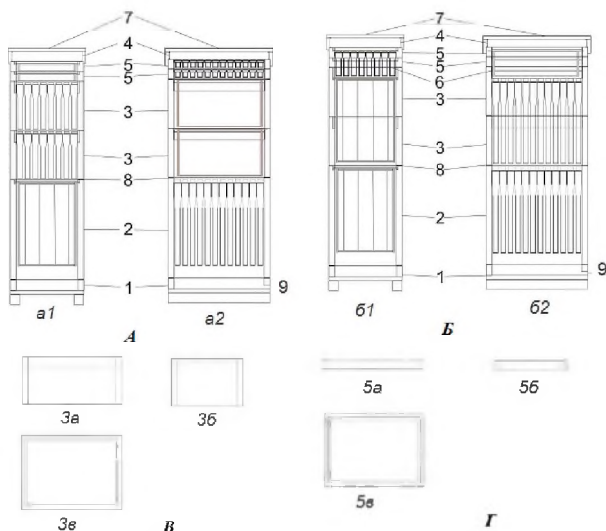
Уніфікований багатофункціональний вулик (А, Б – варіанти повної комплектації; а1, б1 – головний вигляд; а2, б2 – вигляд зліва; В – магазинний корпус; Г – мала надставка); 1 – дно; 2 – гніздовий корпус з 12-ма рамками розміром 300×435 мм; 3 – магазинний корпус; 3а – головний вигляд магазинного корпусу; 3б – вигляд зліва магазинного корпусу; 3в – вигляд зверху магазинного корпусу; 4 – утеплювач; 5 – мала надставка; 5а – головний вигляд малої надставки; 5б – вигляд зліва малої надставки; 5в – вигляд зверху малої надставки; 6 – 8 магазинних рамок розміром 435х230 мм; 7 – дах; 8 – розділювальна решітка; 9 – льоток
